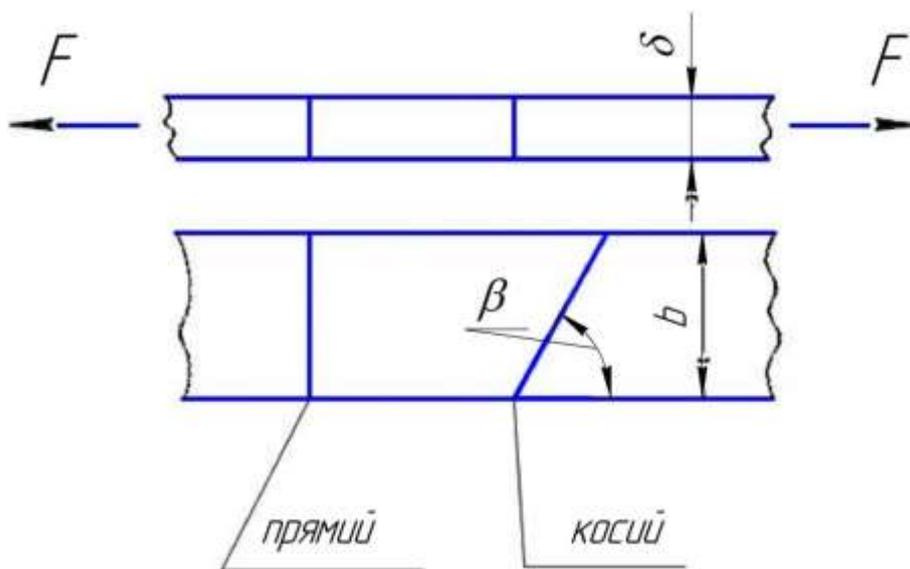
Розрахункова схема зварного з'єднання стиковим швом
